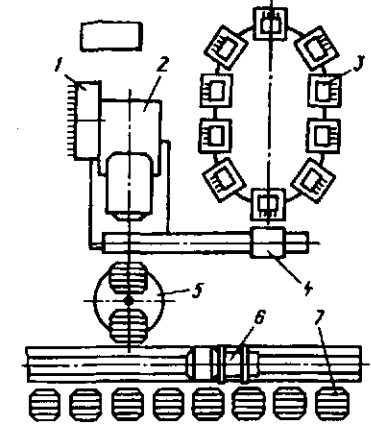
Гибкий производственный модуль с автоматизированными системами смены инструмента из магазина и шпиндельных головок из накопителя: 1 – магазин с инструментами; 2 – станок с ЧПУ; 3 – накопитель шпиндельных головок (коробок); 4 – перегружатель головок; 5 – поворотный стол станка; 6 – рельсовая тележка-загрузчик заготовок; 7 – стэнд-накопитель палет с заготовками
